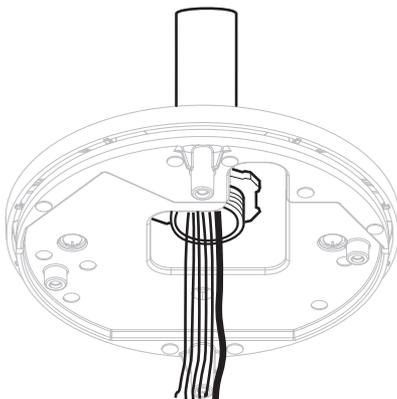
Протягивание проводов: подвесные системы для установки в помещении
